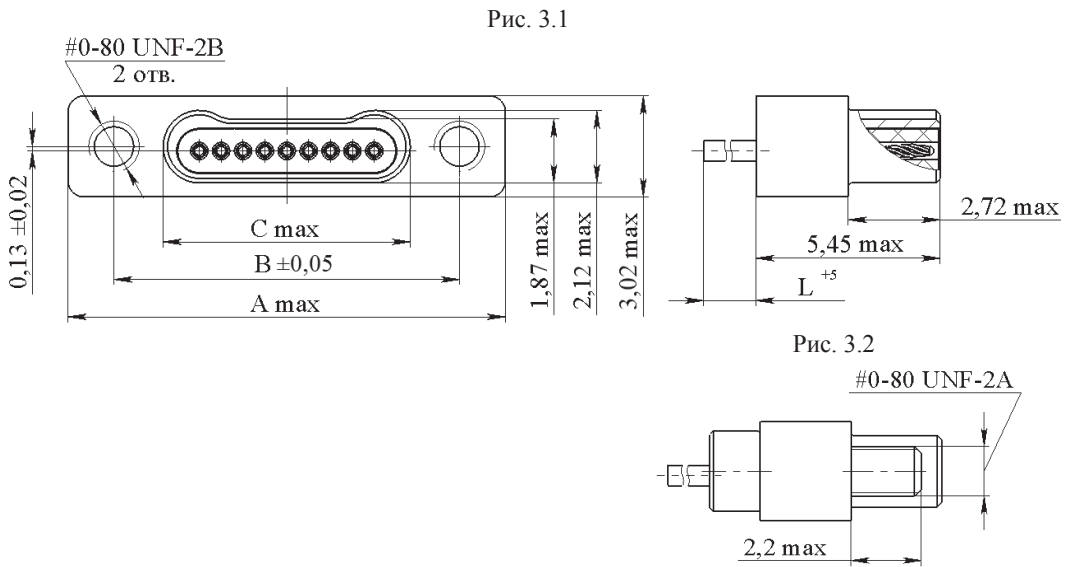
Соединитель СП450-01...1...Ш2...
